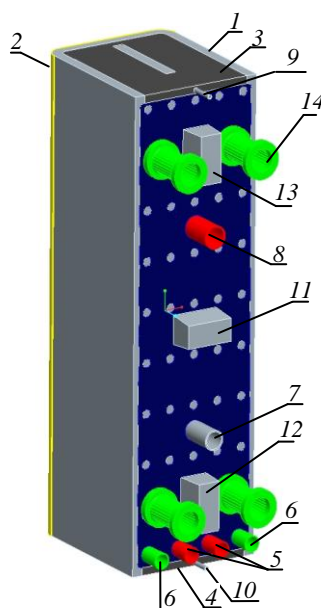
Общий вид КБЛСЭ ИМБ: 1 — скоба ПС; 2 — защитное покрытие ПС; 3 — верхняя крышка корпуса ИМБ; 4 — нижняя крышка корпуса ИМБ; 5 — выходные патрубки PbLi-эвтектики; 6 — входные патрубки PbLi-эвтектики; 7 — входной патрубок He-теплоносителя; 8 — выходной патрубков He-теплоносителя; 9 — входной патрубков газа-носителя; 10 — выходной патрубков газа-носителя; 11 — центральный противомоментный ключ; 12 — нижний противомоментный ключ; 13 — верхний противомоментный ключ; 14 — гибкая механическая опора
